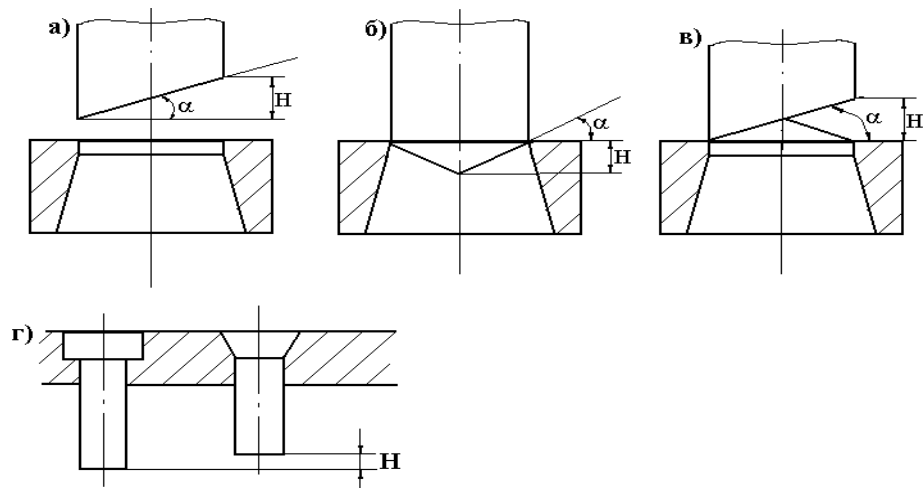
Конструкция инструмента для снижения усилий вырубке-пробивки
